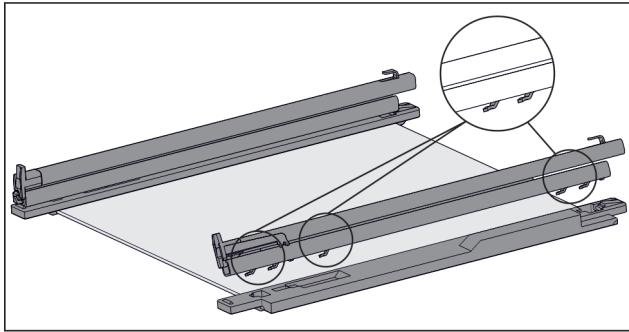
Скляна пластина з рейками та деталями для підтримки
